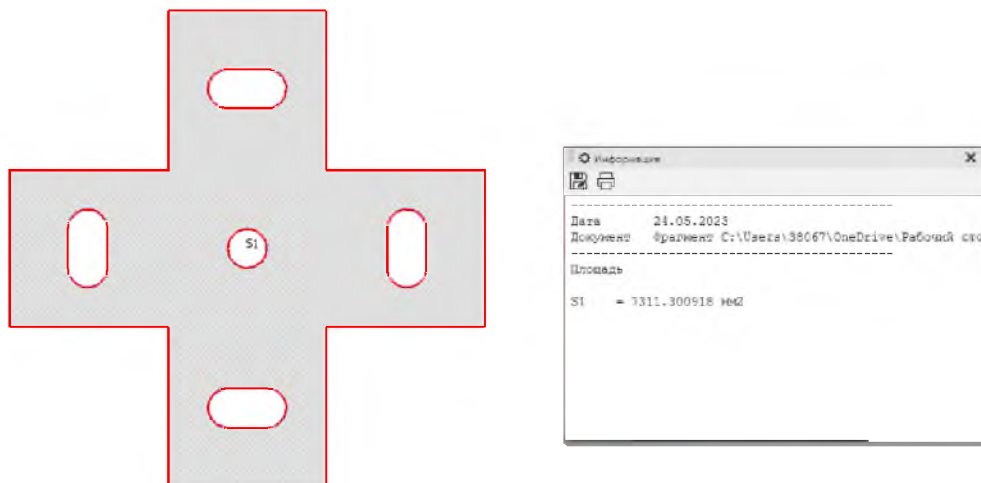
Визначення площі поверхні заготовки деталі
